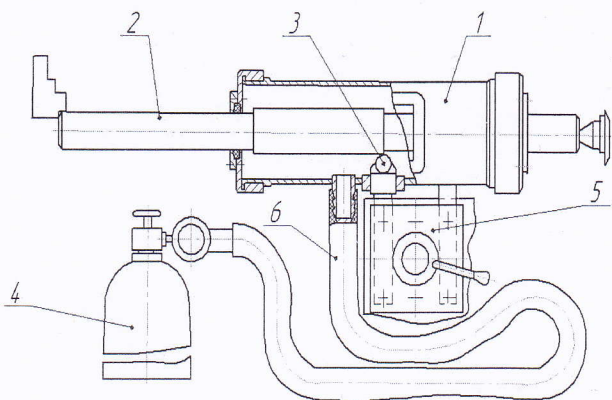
Схема різання в газоподібних середовищах: 1 – камера; 2 – деталь; 3 – різець; 4 – балон з газом; 5 – верстат (різцетримач); 6 – шланг
